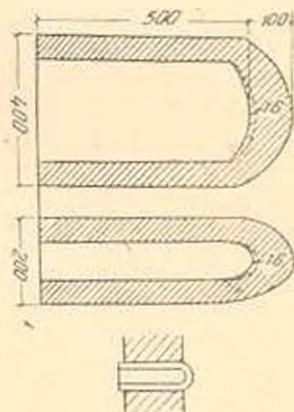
Схема стальных электродов, их разъедания с наружной стороны и расположения в стене ванны печи.
